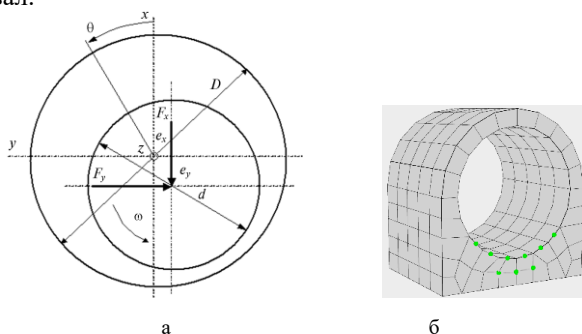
Схема цилиндрического подшипника скольжения (а) и дискретизация конструкции подшипника квазисовместными конечными элементами (б).
